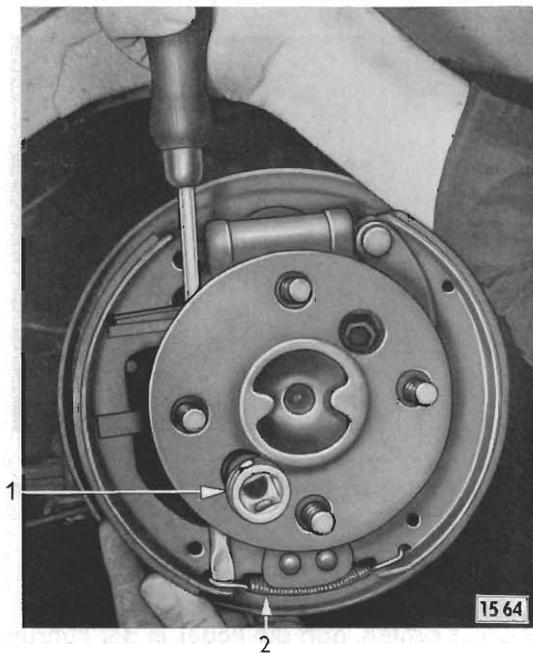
Untere Rückzugfeder aus einer Bremsbacke aushängen
